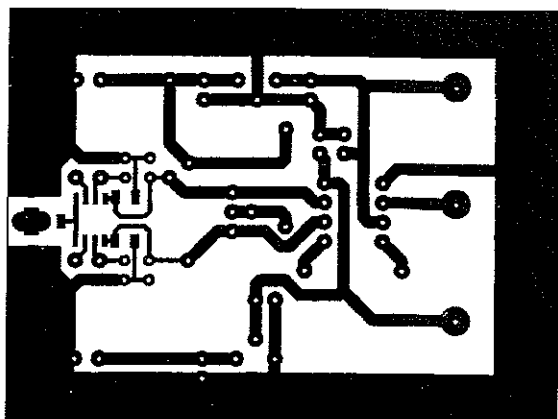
Print-layout til HF-milliwatt forsatsen.
